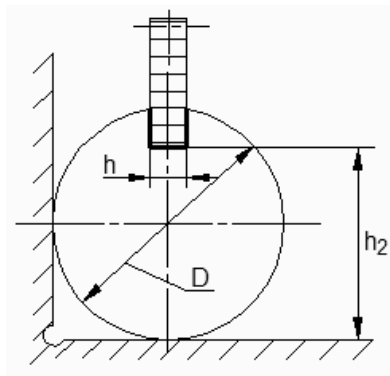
Схема фрезерования шпоночного паза на валу.
